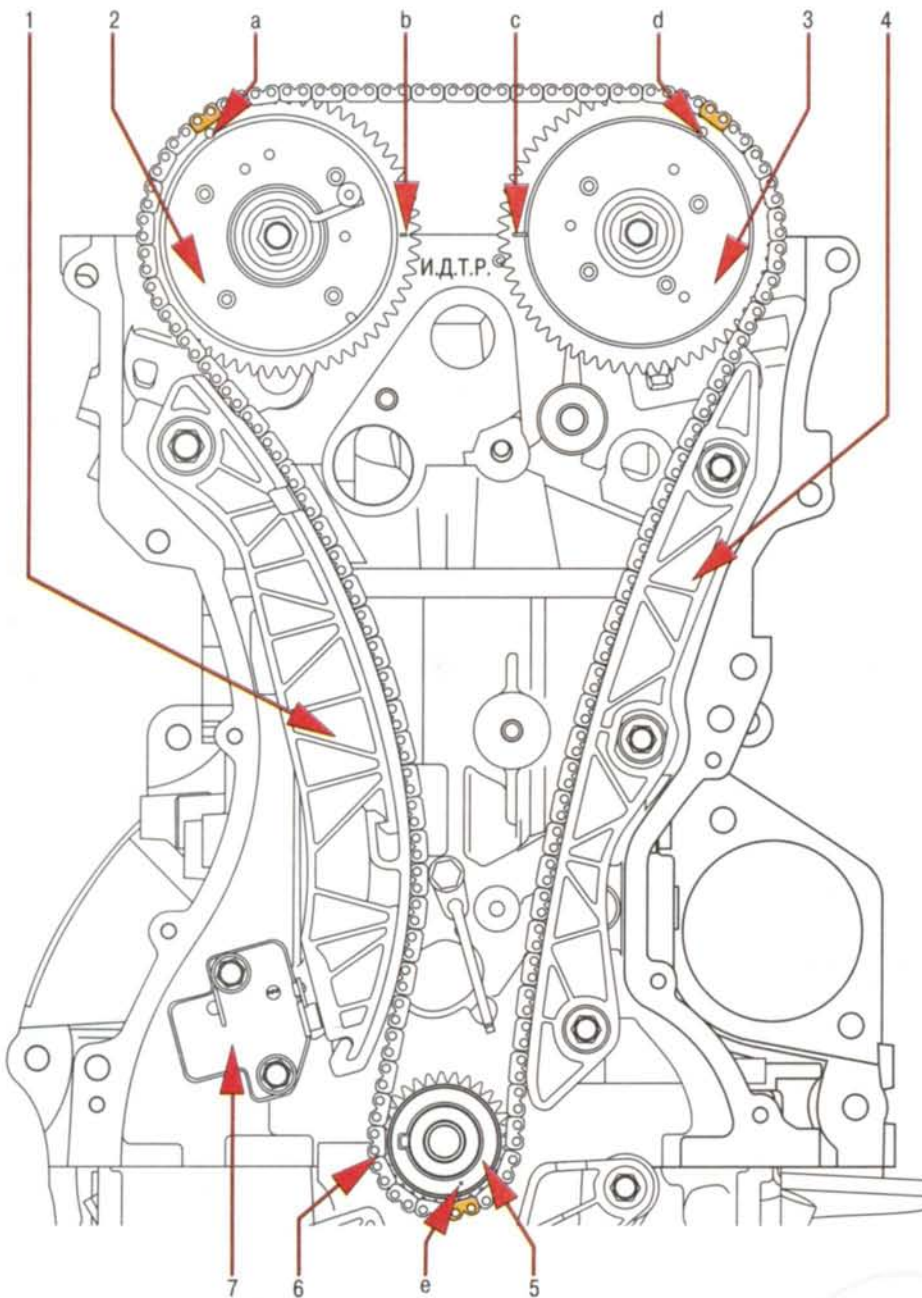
Привод газораспределительного механизма: 1 – башмак натяжителя цепи; 2 – шестерня распределительного вала выпускных клапанов; 3 – шестерня распределительного вала впускных клапанов; 4 – успокоитель цепи; 5 – шестерня коленчатого вала; 6 – цепь привода газораспределительного механизма; 7 – натяжитель цепи; a, b, c, d, e – метки
